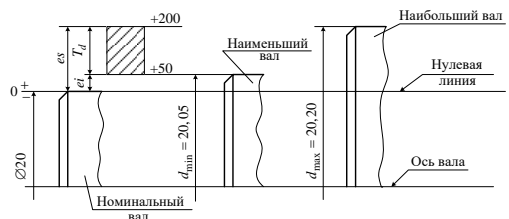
Схема расположения поля допуска на изготовление вала
